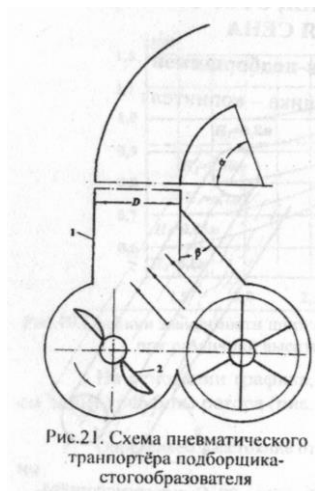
Схема пневматического транспортера подборщика-стогообразователя
